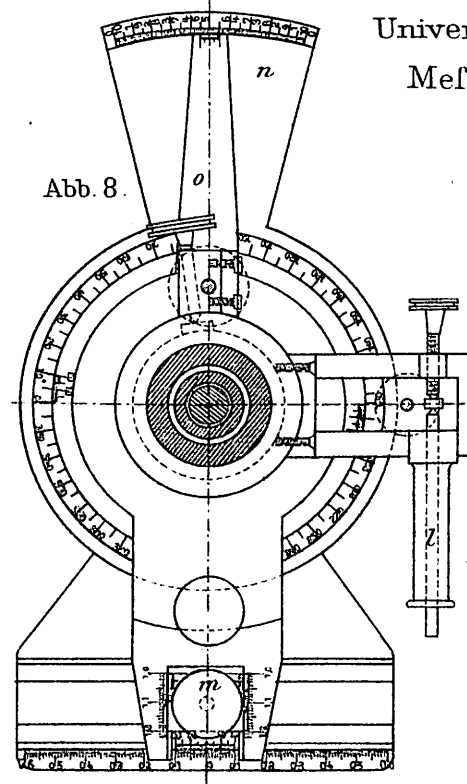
bis 9. Universal-Winkel-Meßwerkzeug.
